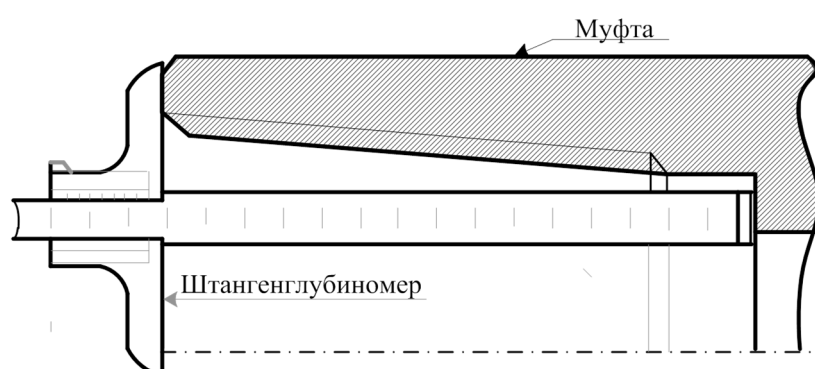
Измерение расстояния от торца муфты до упорного уступа при помощи универсального штангенглубиномера
